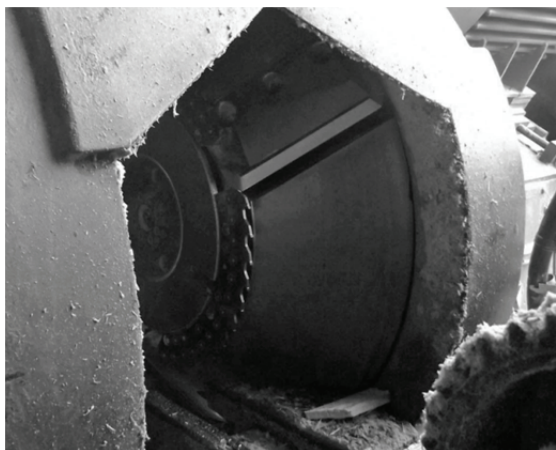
Малоножевая торцово-коническая фреза фрезерно-брусующего станка
